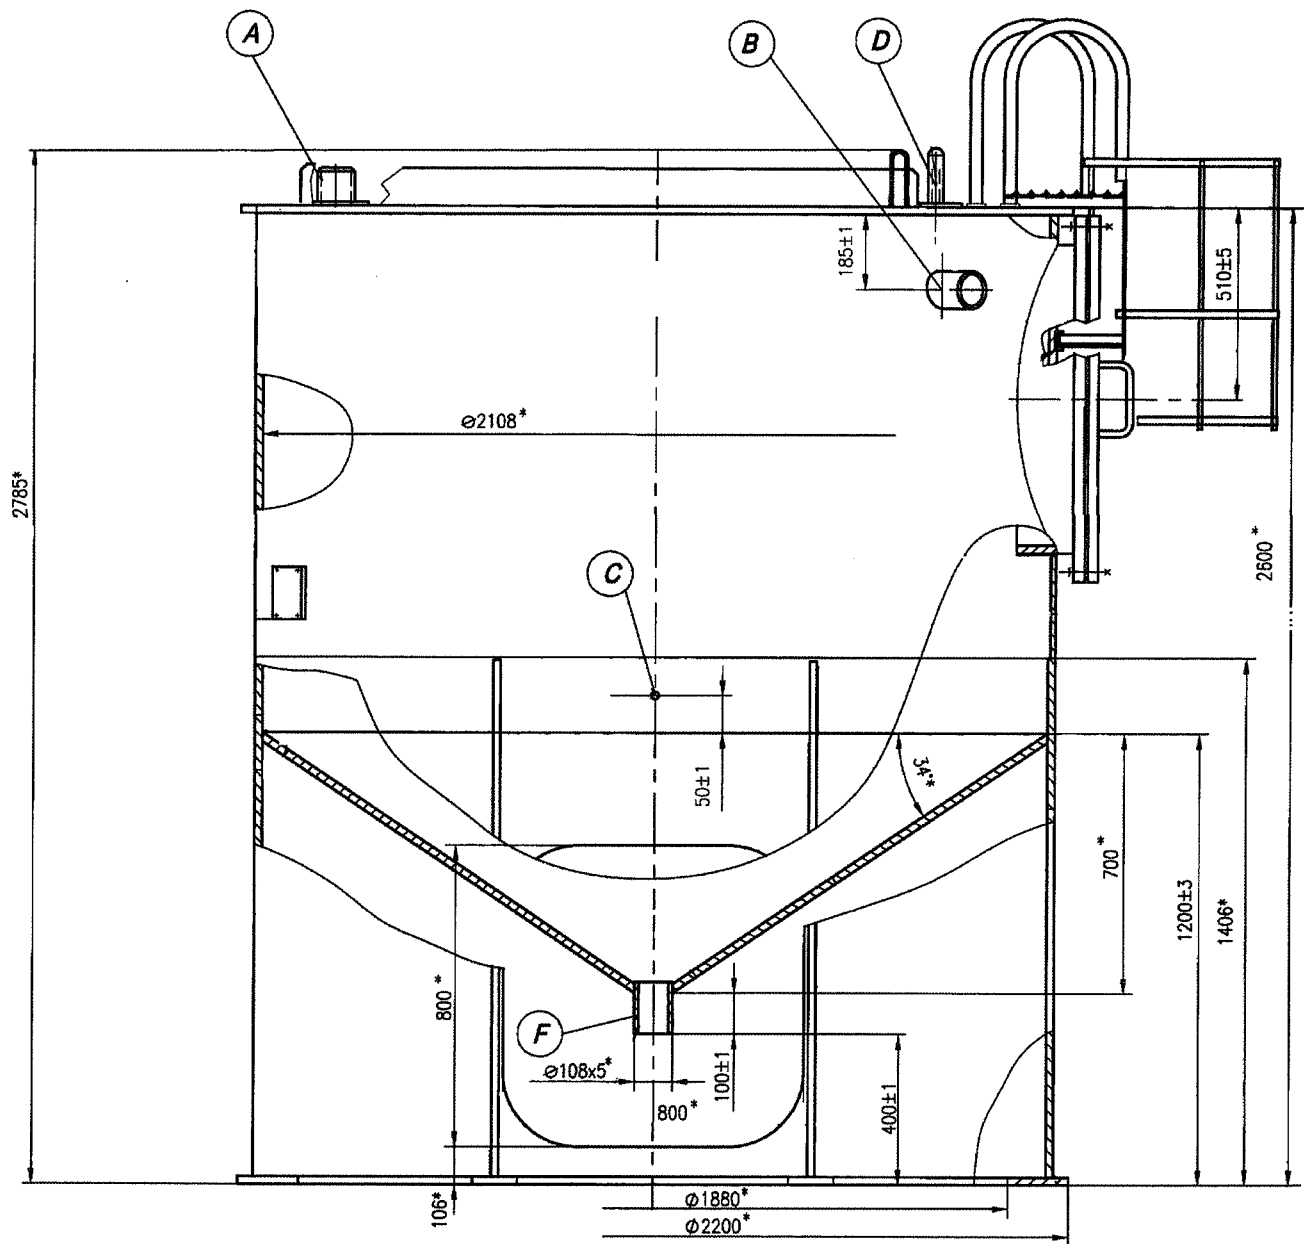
Габаритный чертеж бака сбора конденсата вспомогательного корпуса
